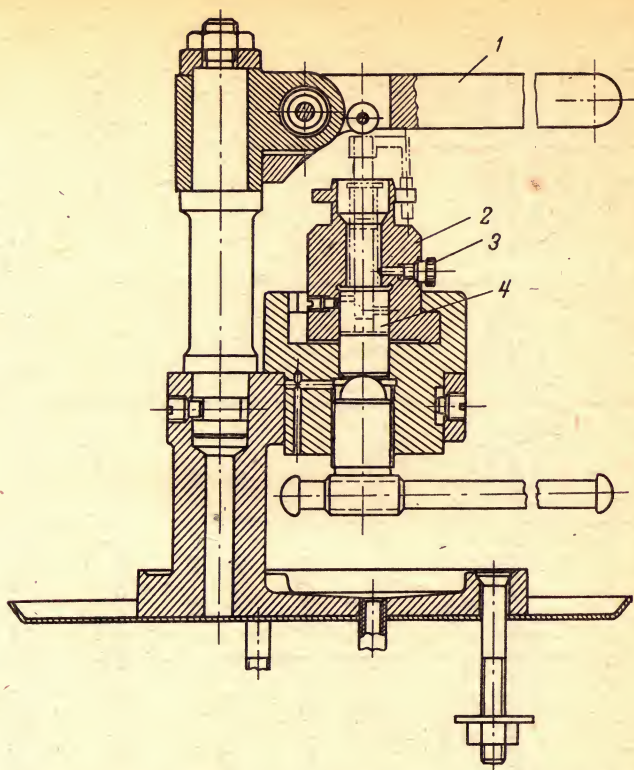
Прибор КИ-759 для проверки гидравлической плотности плунжерных пар:
